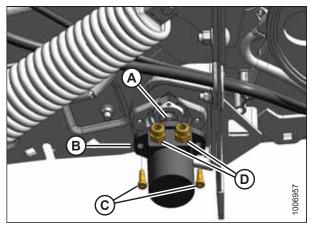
Moteur hydraulique arrière - Côté gauche
